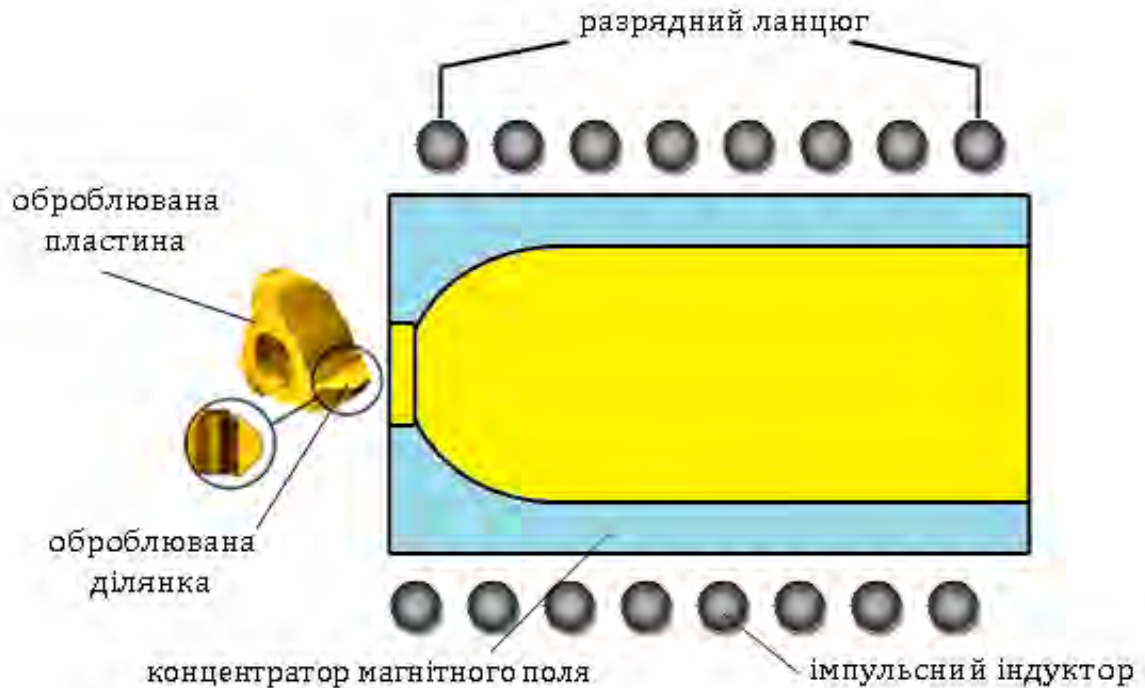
Торцева схема обробки поверхні твердосплавних змінних багатогранних пластин
